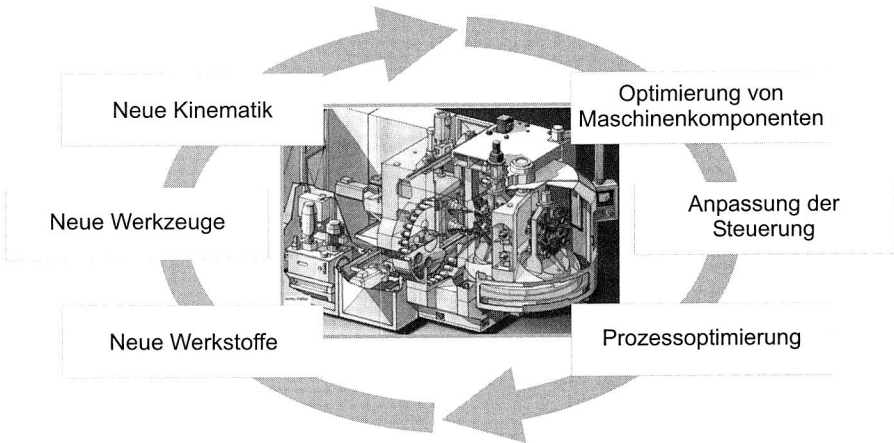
Stetiger Kreislauf der Werkzeugmaschinenentwicklungen
